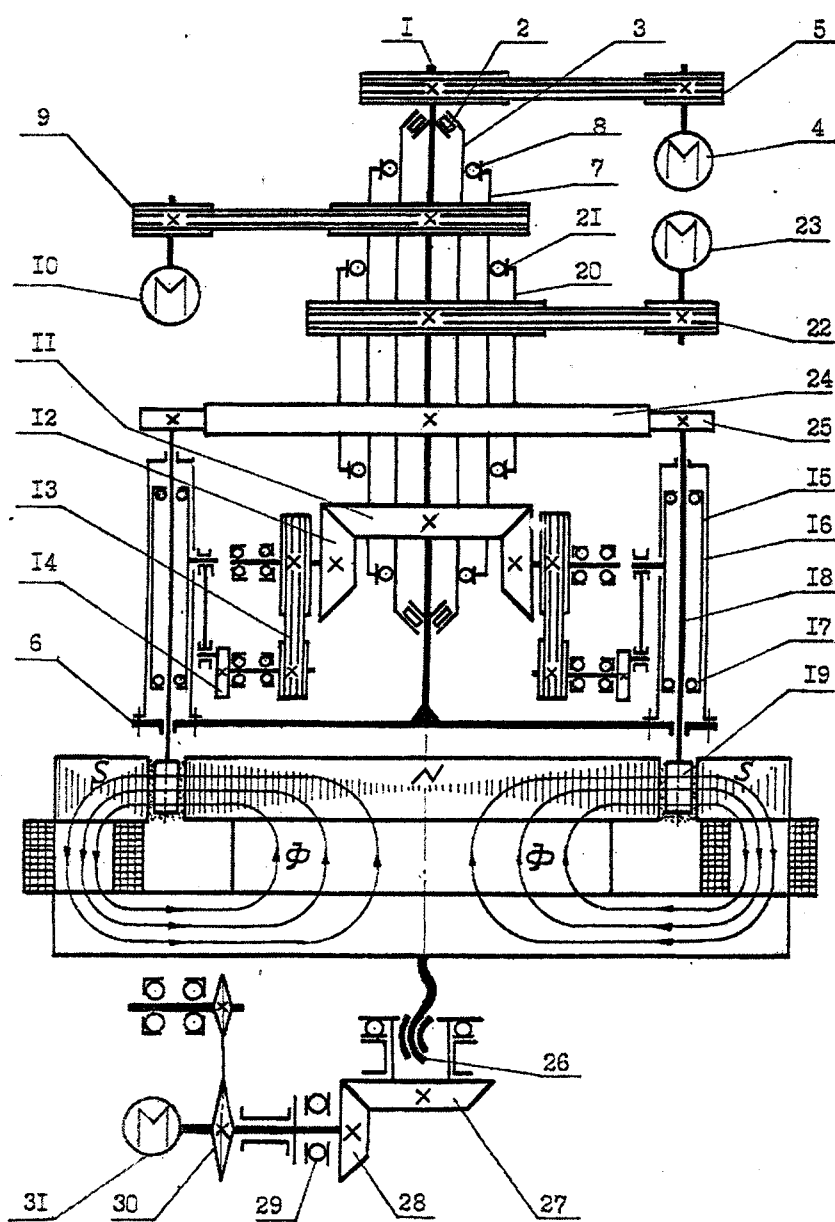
Кинематическая схема магнитно-абразивного роторного станка модели МАРС.
